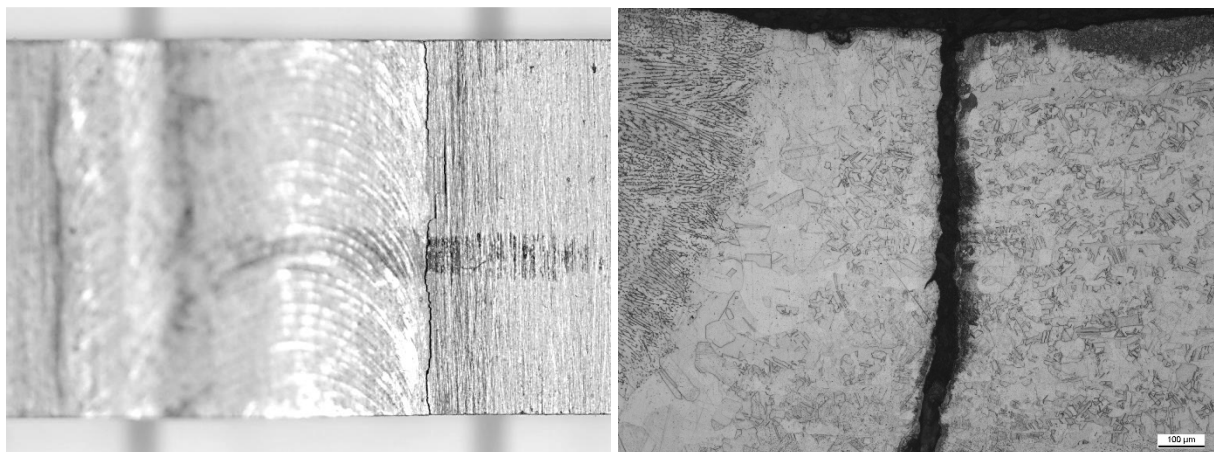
Anrissort geschweißter Rohrsegmentproben; links: Proben-Draufsicht; rechts: Anriss im Querschliff
